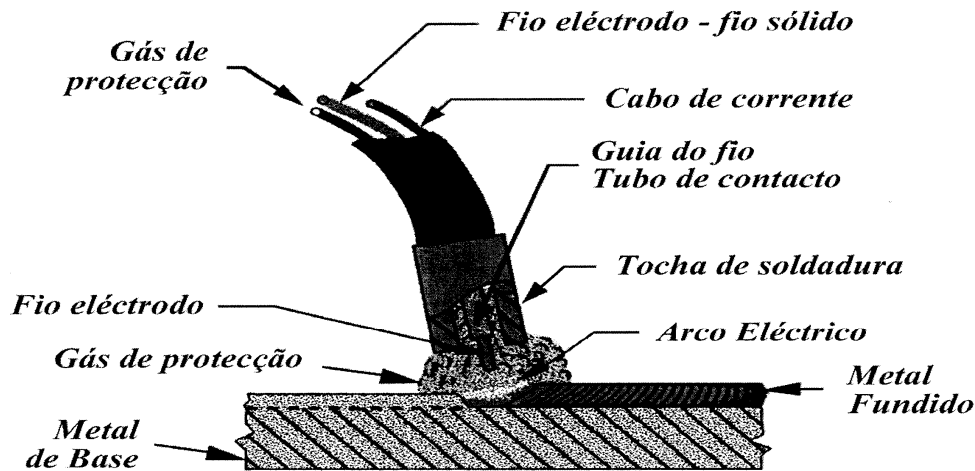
Esquema de soldadura do processo GMAW
